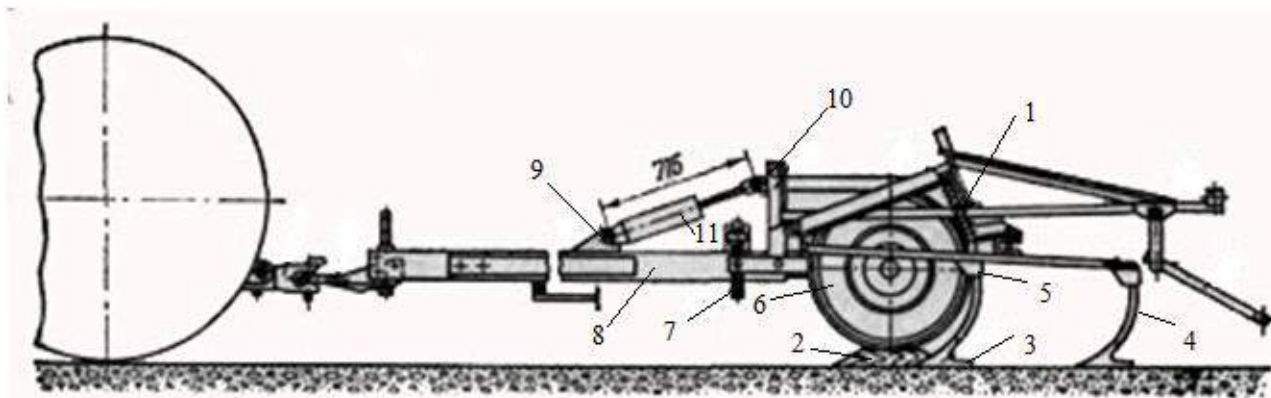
Схема регулировки рабочих органов культиватора КПС - 4 на заданную глубину обработки почвы:
